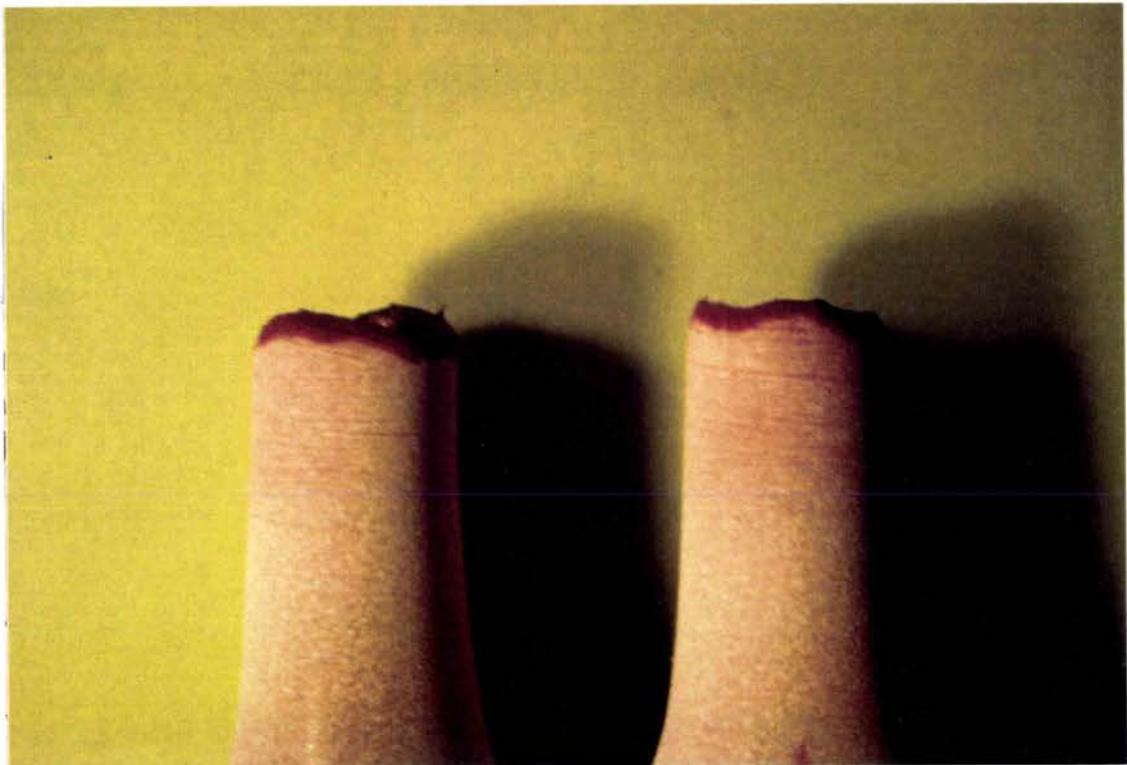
Fissurations secondaires sur une éprouvette à rupture
